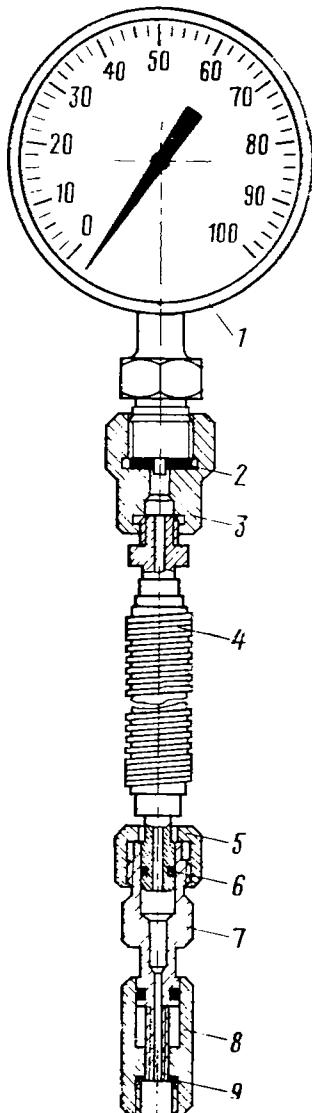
Приспособление для замера давления в цилиндрах подвески:
